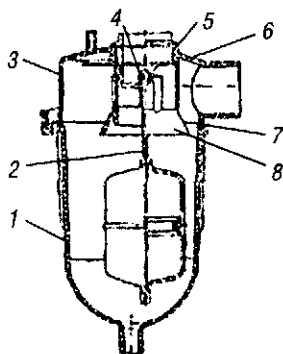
Схема предохранительной камеры: 1 – корпус; 2 – поплавок; 3 – крышка; 4 – кольцо; 5 – шайба; 6 – отражатель; 7 – прокладка; 8 – гайка
